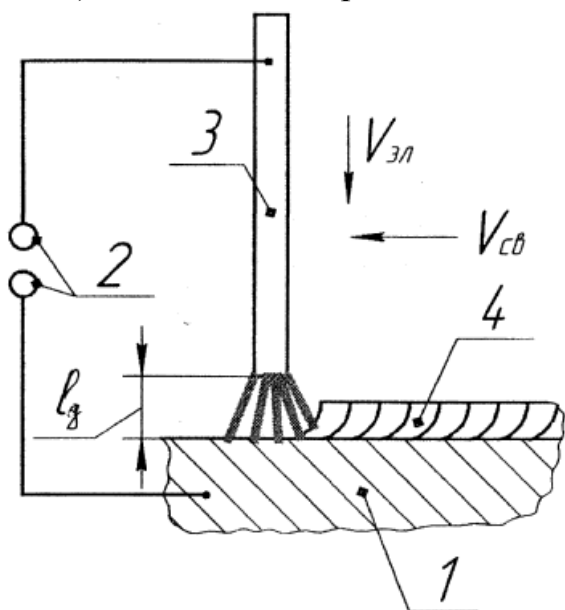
Схема ручной электродуговой сварки: 1- свариваемое изделие; 2-источник сварочного тока; 3- плавящийся электрод; 4- сварной шов; $V_{эл}$ - скорость подачи электрода, м/ч; $V_{св}$ - скорость сварки, м/ч; $l_д$ - длина сварочной дуги, мм.
